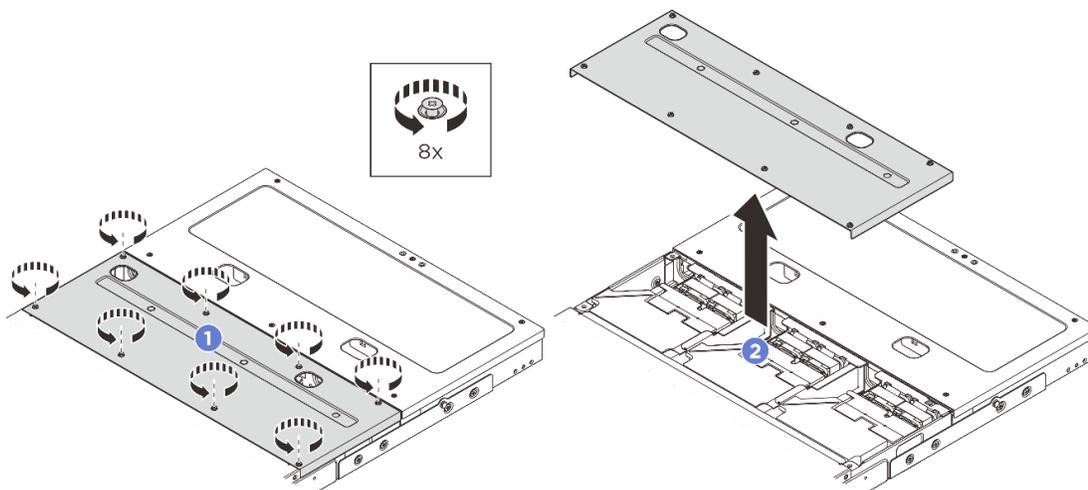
Снятие среднего верхнего кожуха корпуса 1U3N
